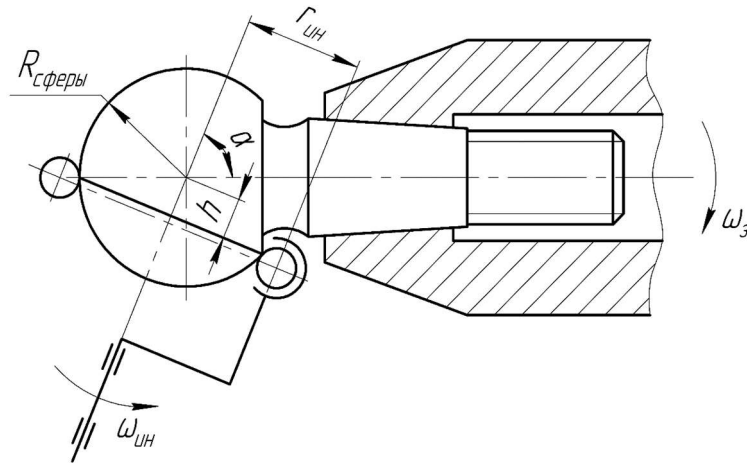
Схема обкатывания неполных сферических поверхностей
